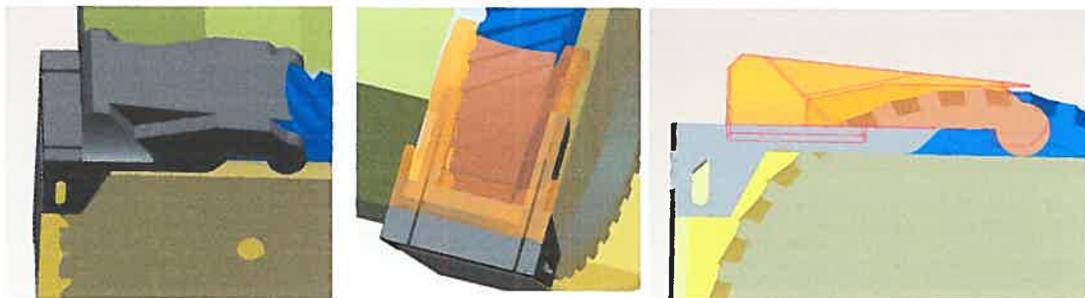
Dessins de la machine pour visualiser les tolérances entre le guide et la meule.¹⁴⁰
